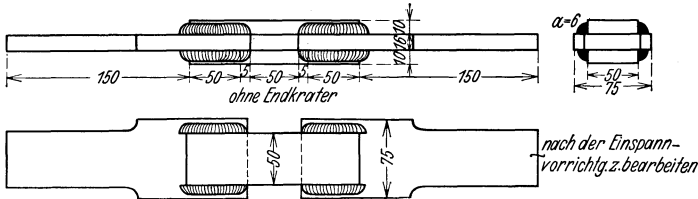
Skizze für Scherproben als Prüfung der Flankenschweißung.
